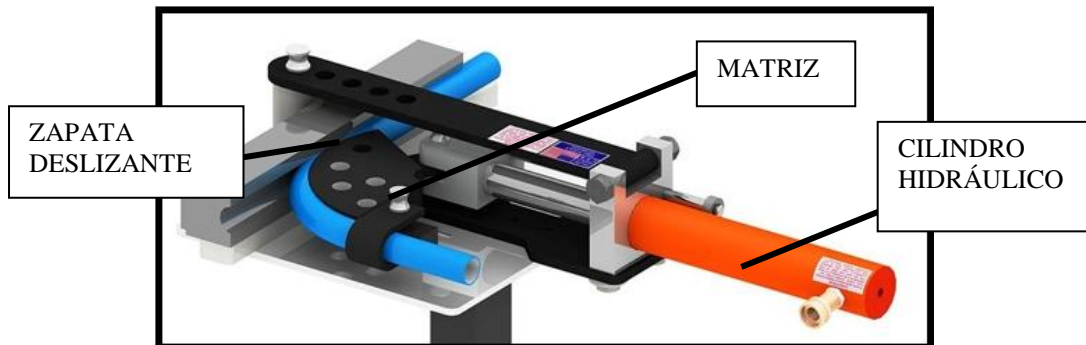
Dobladora hidráulica Pro-Tools HB 302
